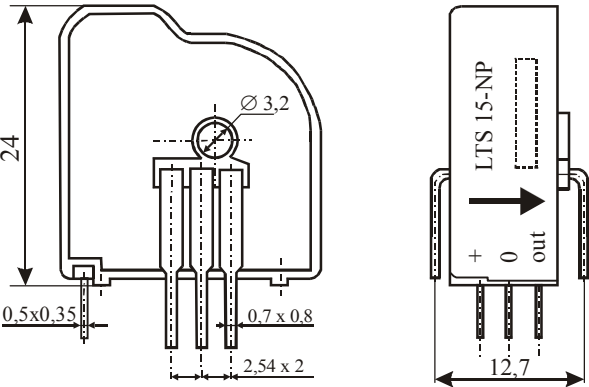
Внешний вид и габаритные размеры датчиков тока типа LTS 15-NP, LTS 25-NP
